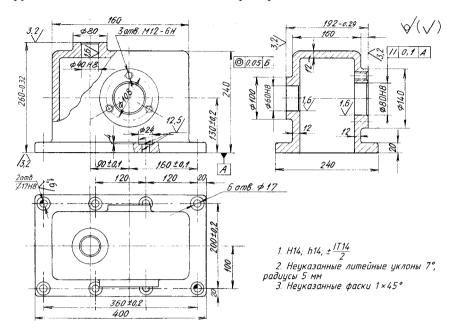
Чертеж детали с конструкторско-технологическим кодом 501127.78931.114300
